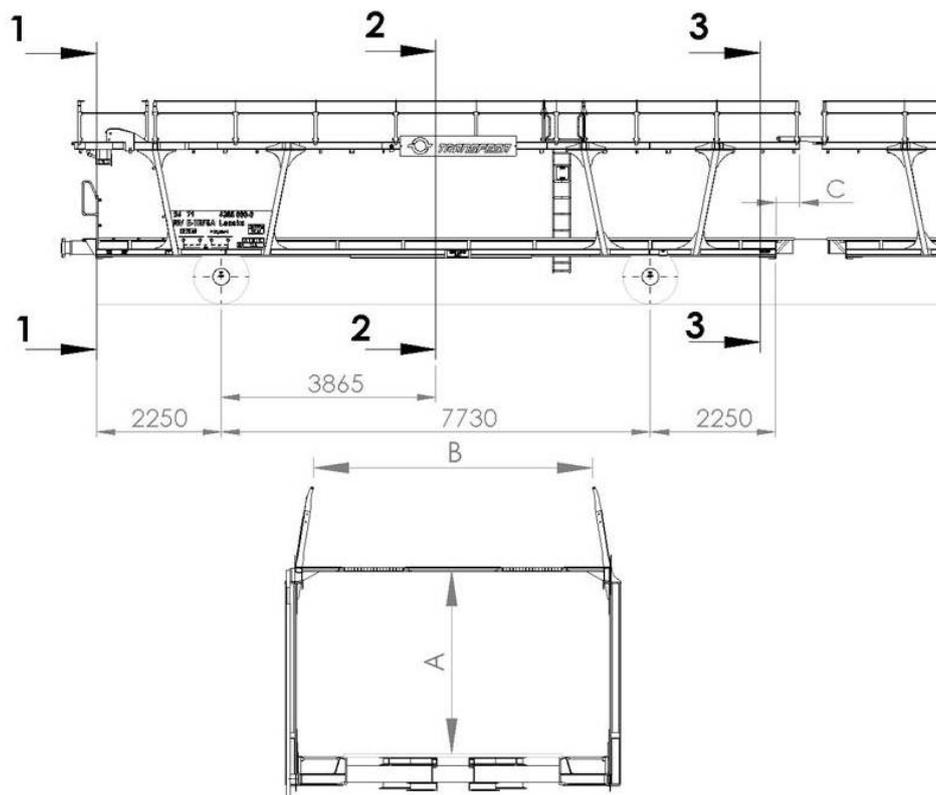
Puntos a comprobar una vez soldado el piso superior.
